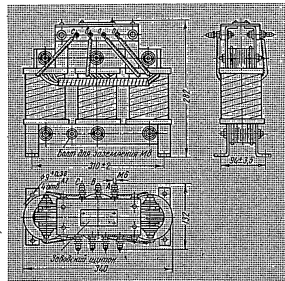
Габаритные размеры трансформатора напряжения типа НТС-05.
